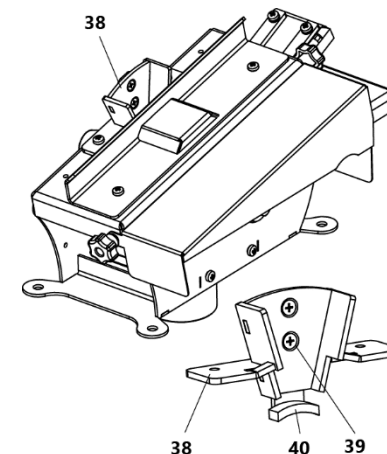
Общий вид приставки с установленным сверлильным патроном
